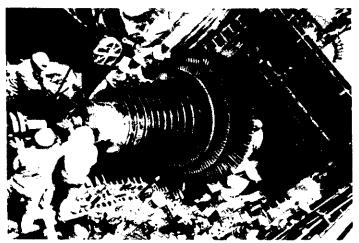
Se observa el rotor de una turbina de vapor de una capacidad de 110 mw, en el momento del montaje del rotor en la carcasa inferior, turbinade 13 ruedas de álabes, 10 de alta presión y 3 de baja presión
